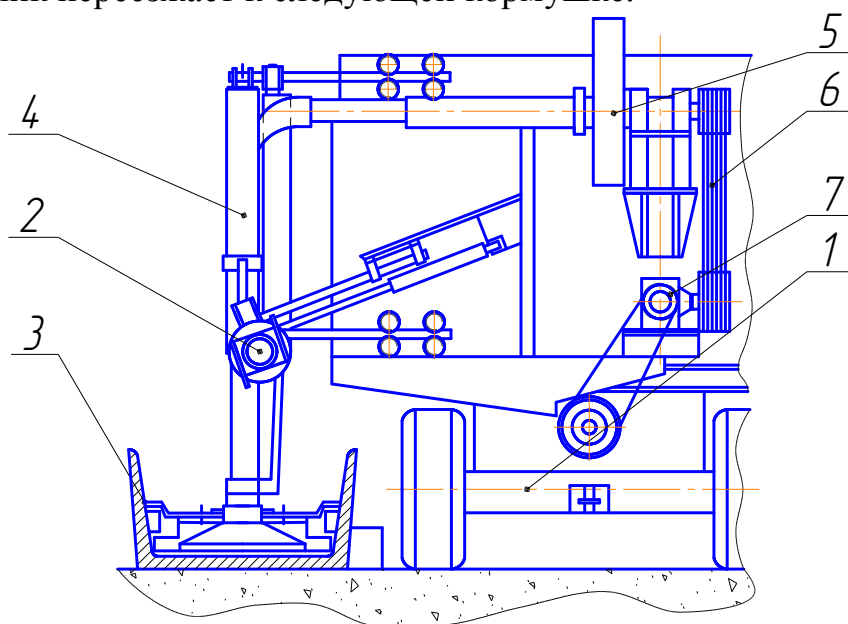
Агрегат для раздачи кормов и уборки их остатков 1 – ходовая часть; 2 – гидромотор; 3 – кормушка; 4 – рукав всасывающий; 5 – вентилятор; 6 – передача ременная; 7 – электродвигатель.
